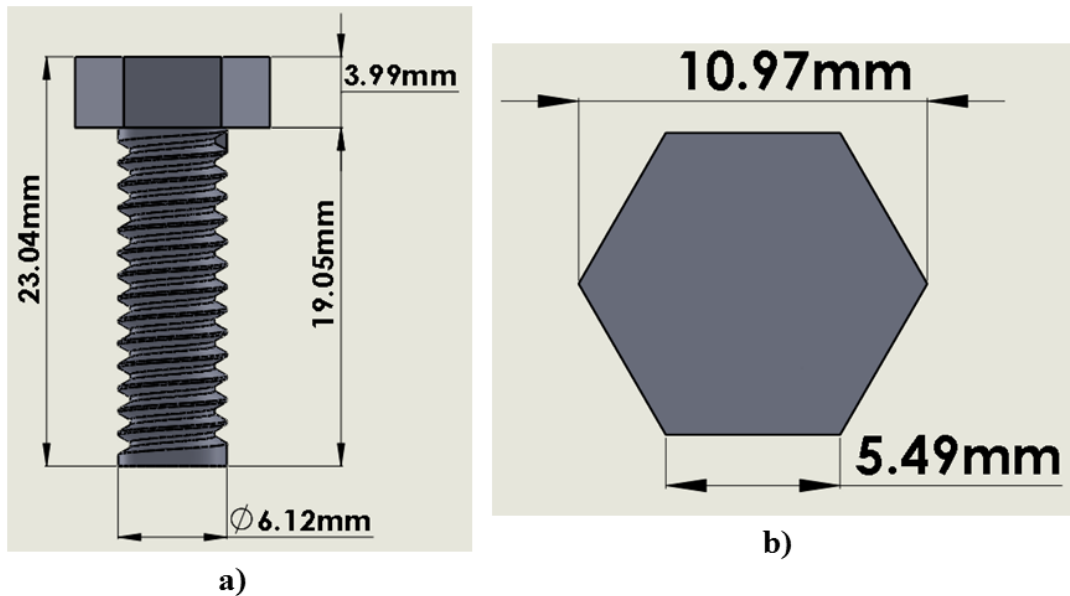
a) Vista frontal del tornillo a utilizar para sujetar la tapa del rodamiento, b) Vista superior del tornillo.
